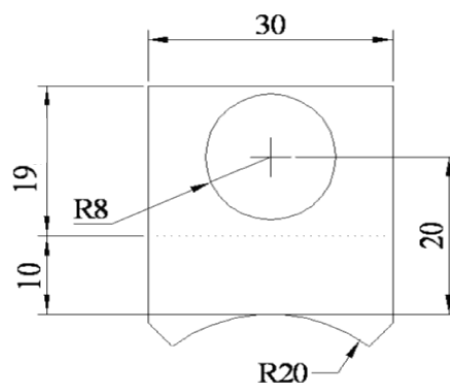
9. Plano de la probeta para ensayo de desgaste (distancia en mm).
